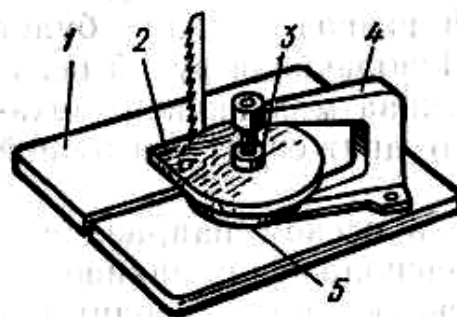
Приспособление для выпиливания круглых деталей на ленточнопильном столярном станке: 1 — стол, 2 — заготовка, 3 — зажимное устройство, 4 — скоба, 5 — диск
